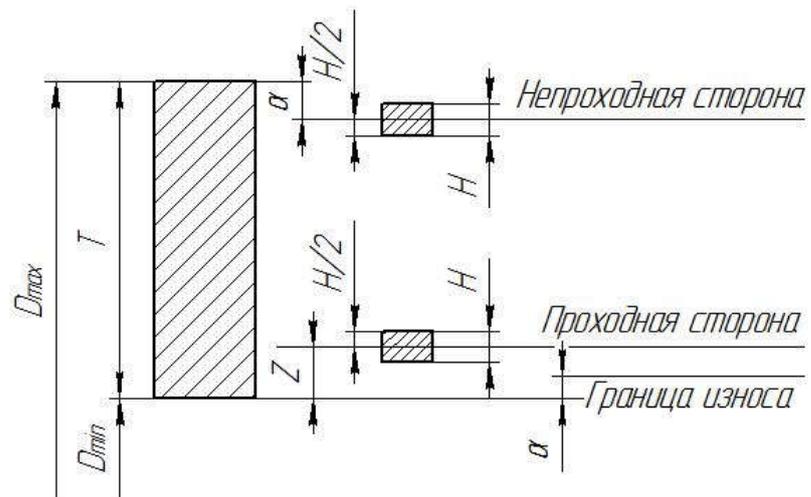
Расположение интервалов допусков для контроля отверстий
